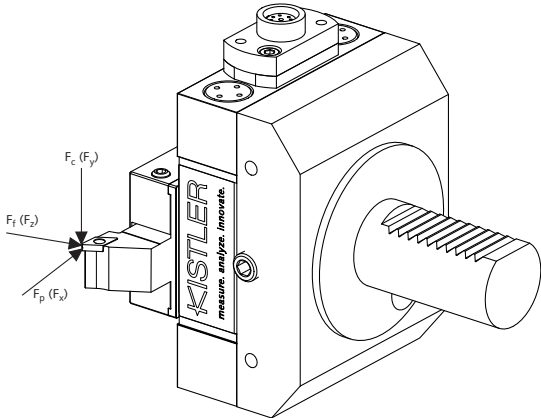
Динамометр типа 9119AA2 с держателем инструмента типа 9119AE16 и фиксатором инструмента VDI типа 9119AB30S
